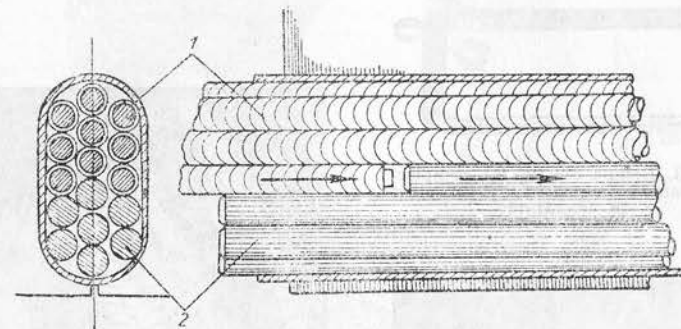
Execuția bobinajului țesut: 1 — sârmă de cupru izolat; 2 — vergele de oțel.
